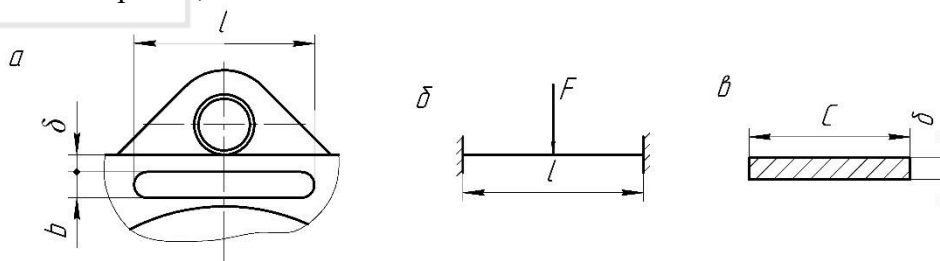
Схеми пружної ділянки: а - конструктивна; б – розрахункова і в – поперечний перетин
